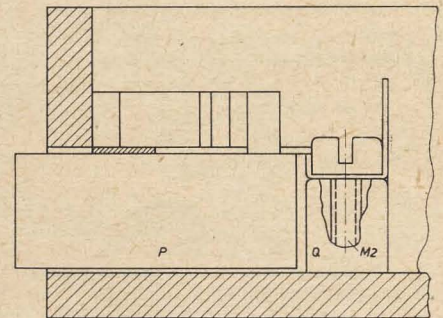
Befestigung des Knoppotentiometers P_1 am Gehäuse
